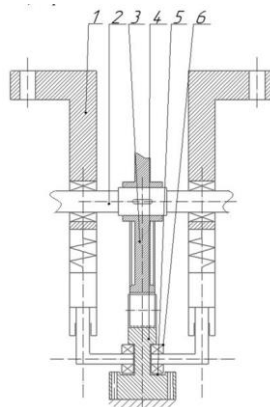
Опорно-направляючий пристрій для зубчато-рейкових рушіїв шахтних електровозів
